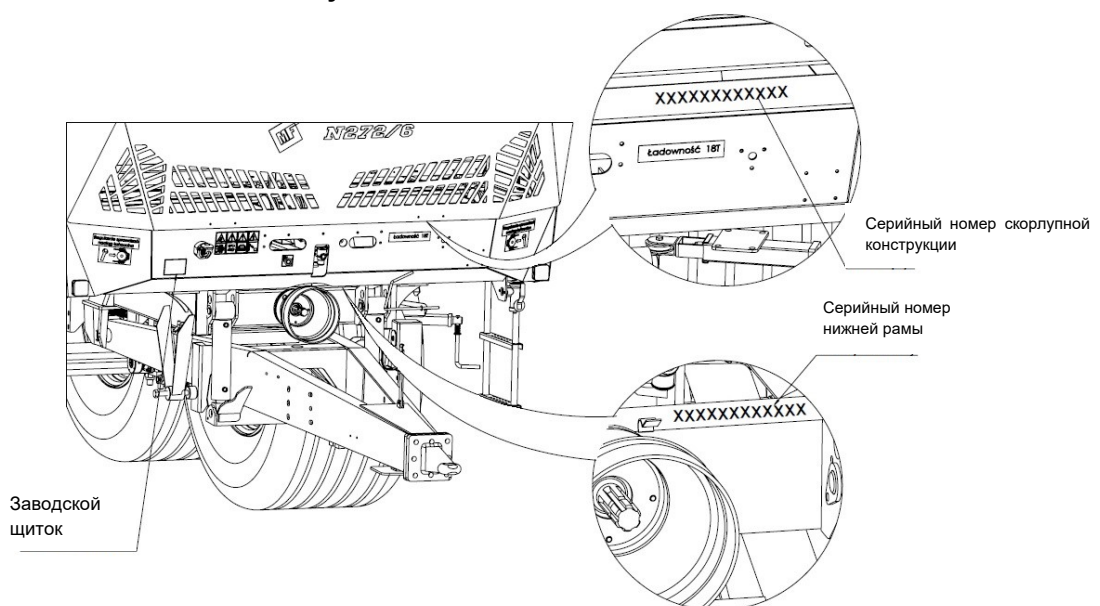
й. Место расположения заводского щитка и серийного номера
